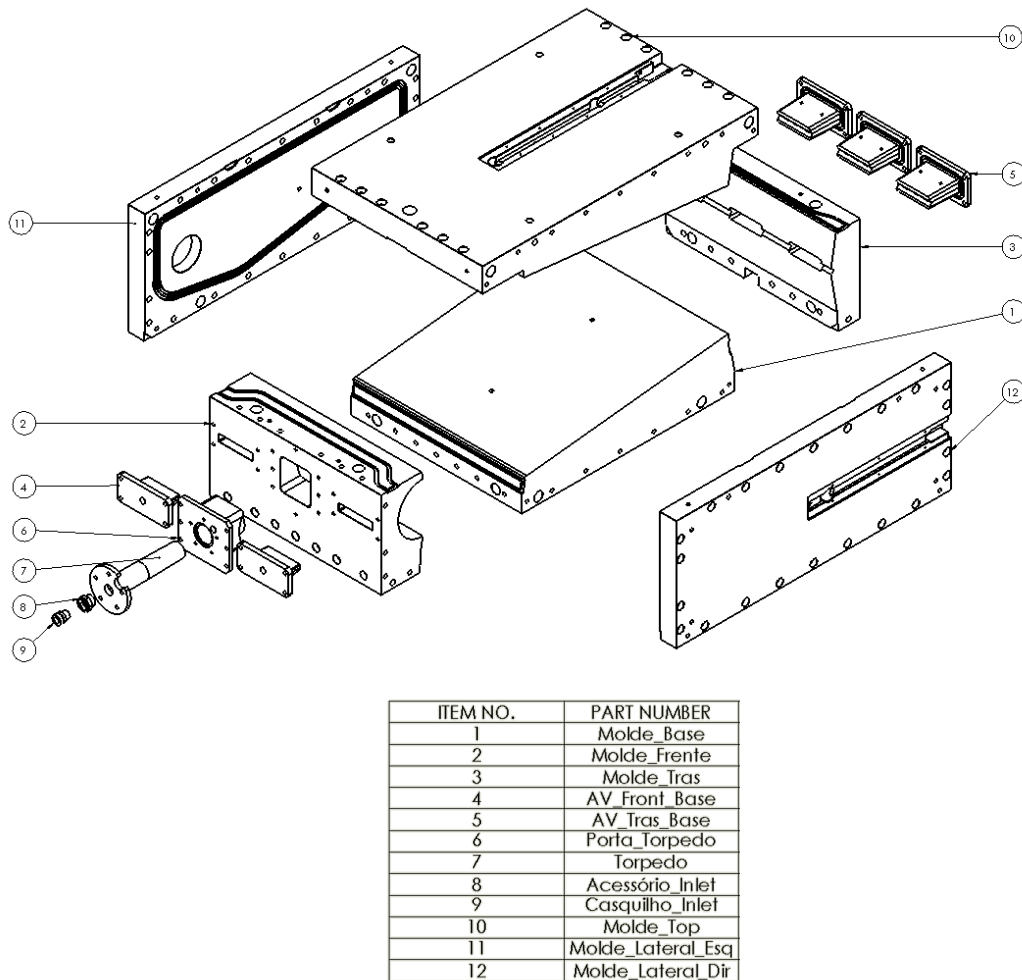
Vista explodida do molde exterior do demonstrador.
